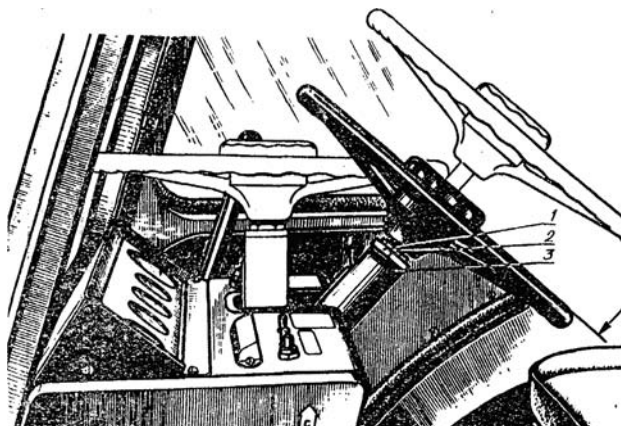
Регулировка рулевой колонки: 1 — гайка; 2 — контргайка; 3 — втулка.
